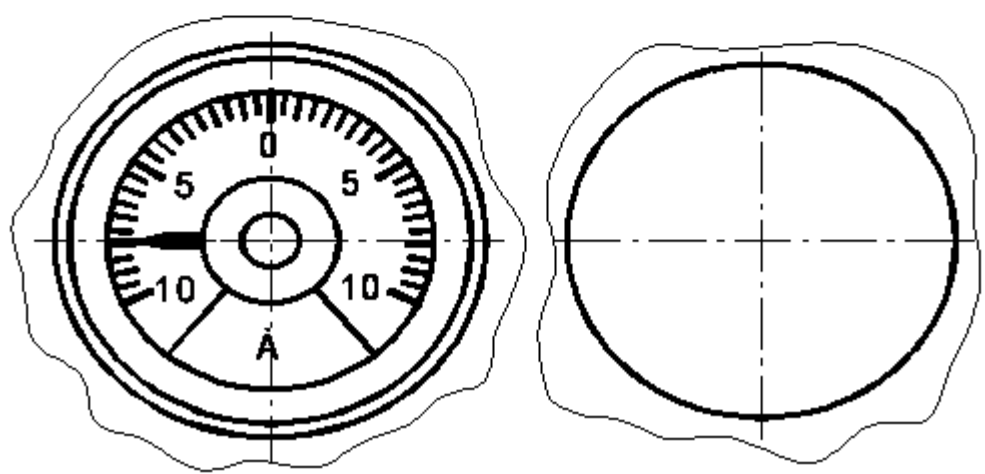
Габаритный чертеж прибора М1611.2-2
